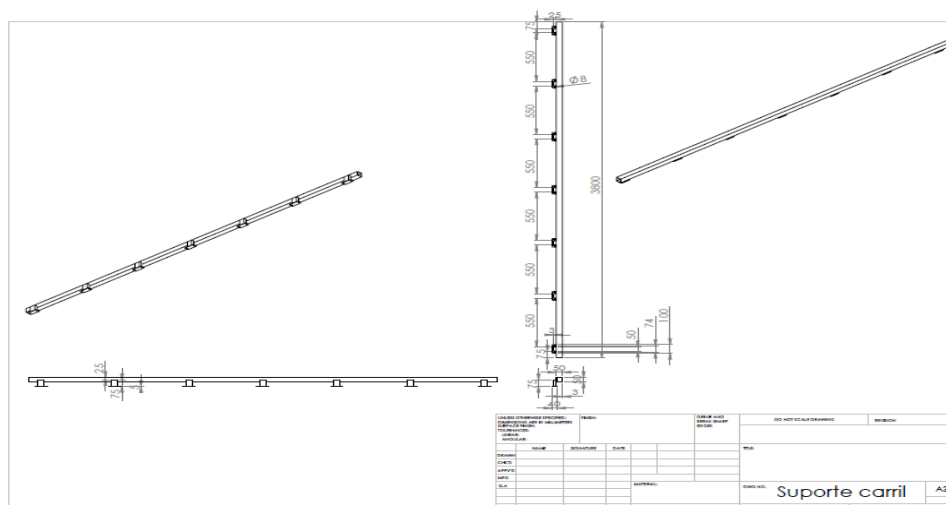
A estrutura desenhada no SolidWorks, com dimensões em milímetros.
